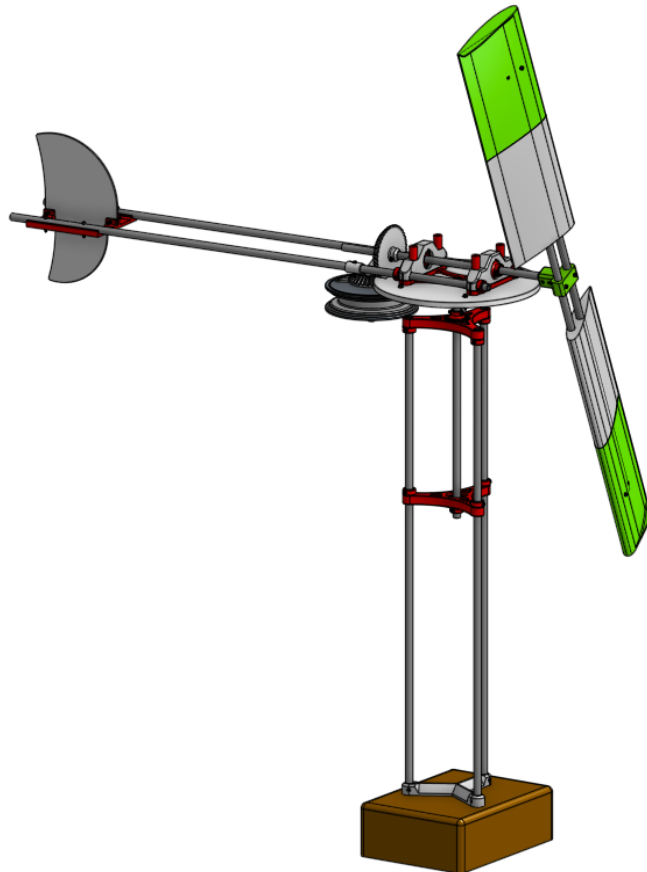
Ensamblaje mecánico completo de la turbina eólica en Onshape [fuente: elaboración propia]
